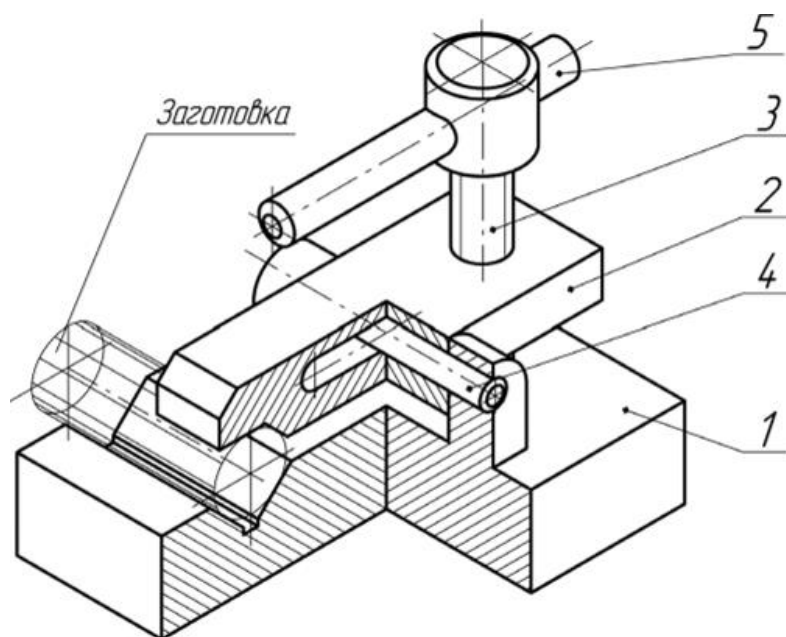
Приспособление для закрепления прутков (Зажим) [14]
